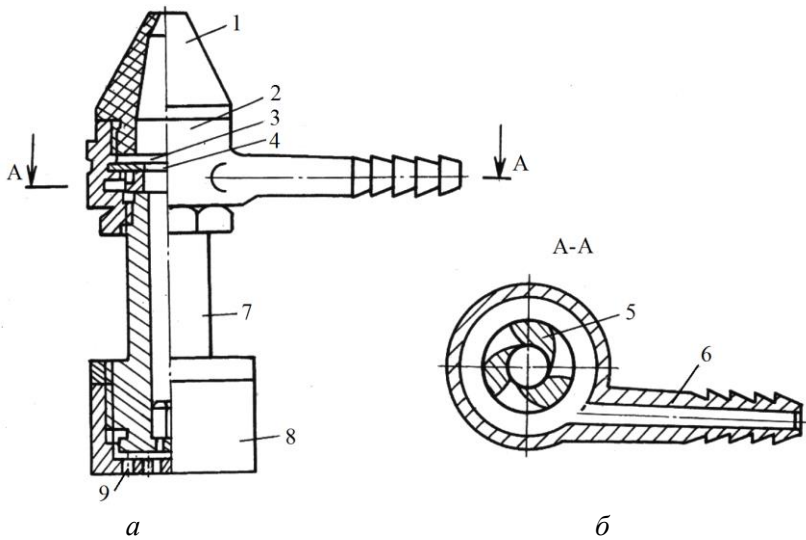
Продольный (а) и поперечный (б) разрез цилиндрической вихревой трубы: 1 – сопло; 2 – корпус; 3 – вихревая камера; 4 – дроссельная шайба; 5 – крыльчатка; 6 – подводной патрубков; 7, 8 – тело трубы и ее заглушка; 9 – отводящие отверстия
